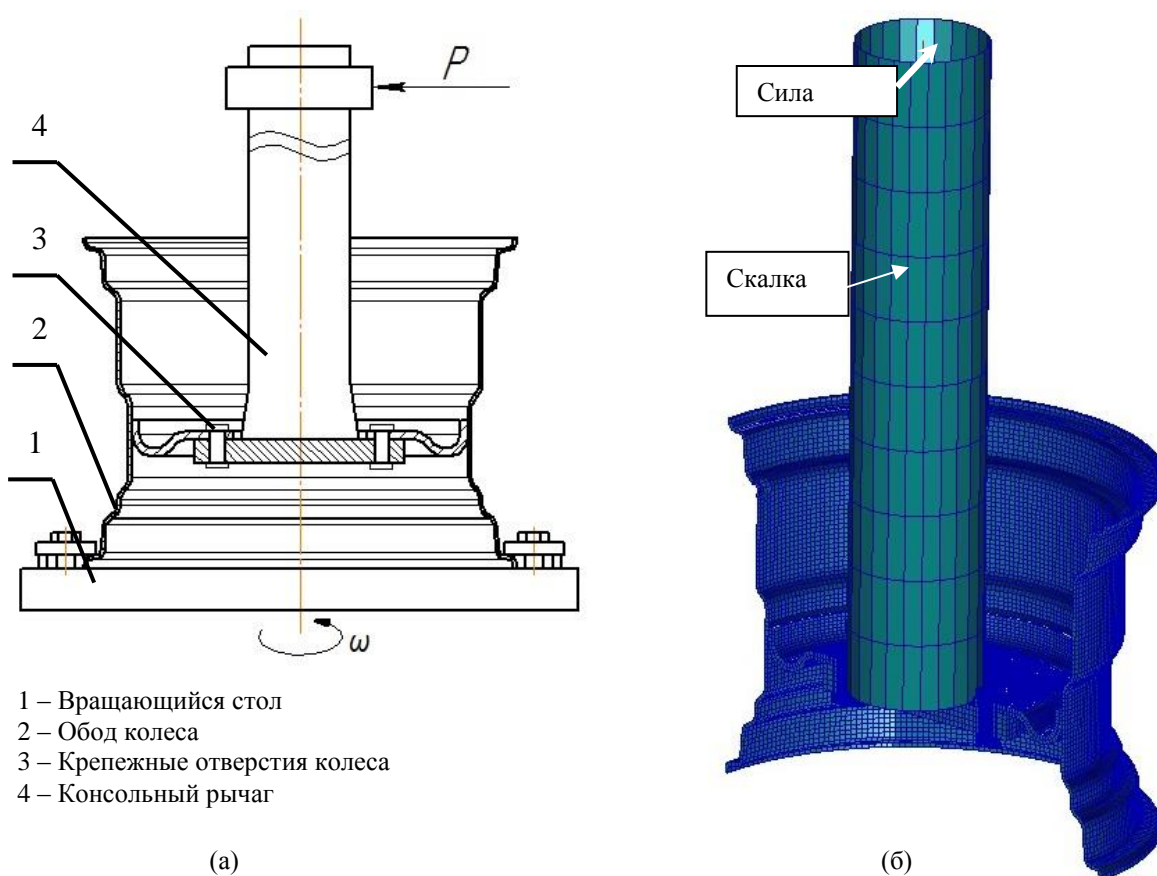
Схема и внешний вид стенда для проведения испытаний на изгиб с вращением (а) и КЭ-модель конструкции в сборе с испытательным стендом (б)
